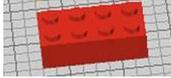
PLANO DE MONTAJE – CENTRO DE TRABAJO 1.
